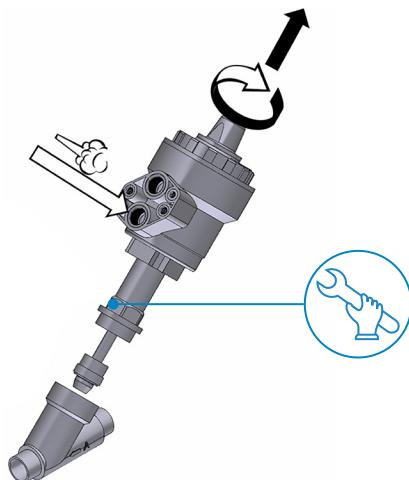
Визуальное изображение этапов демонтажа привода с корпуса клапана.
